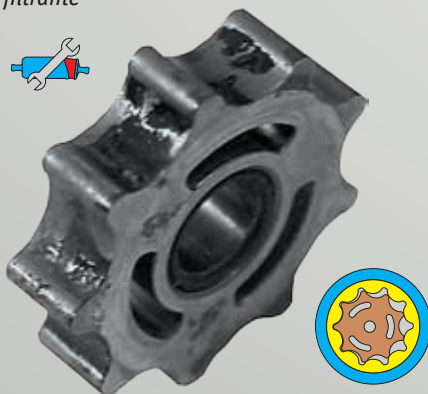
Pasta obturadora en el mecanismo de bombeo (engranaje toroidal)
